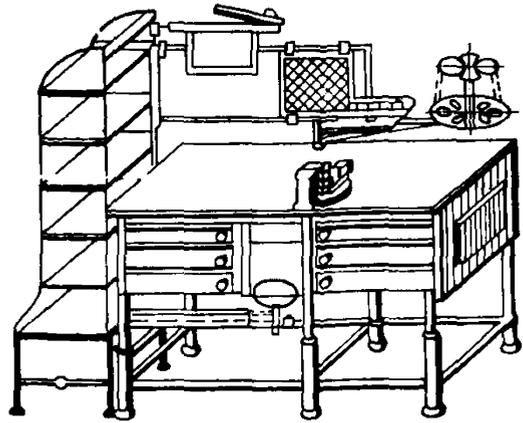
Верстак слесарный предназначен для оборудования рабочего места слесаря
